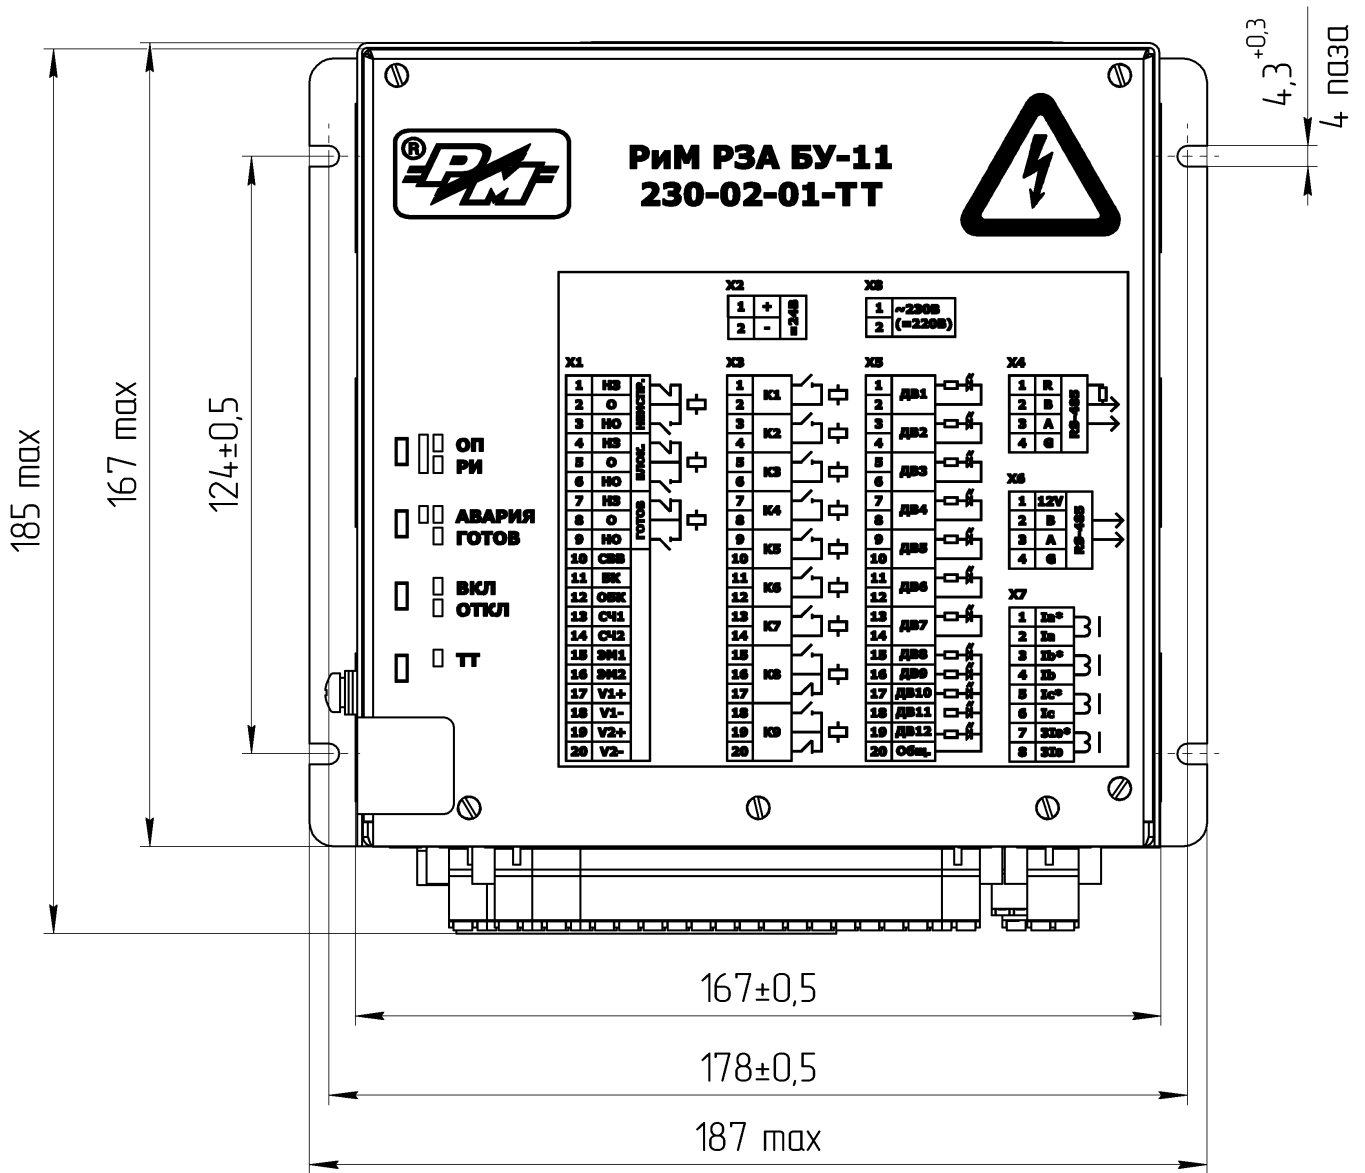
Габаритные и установочные размеры устройств РЗА с кодом конструктивного исполнения 02 (установка на панель монтажную)
